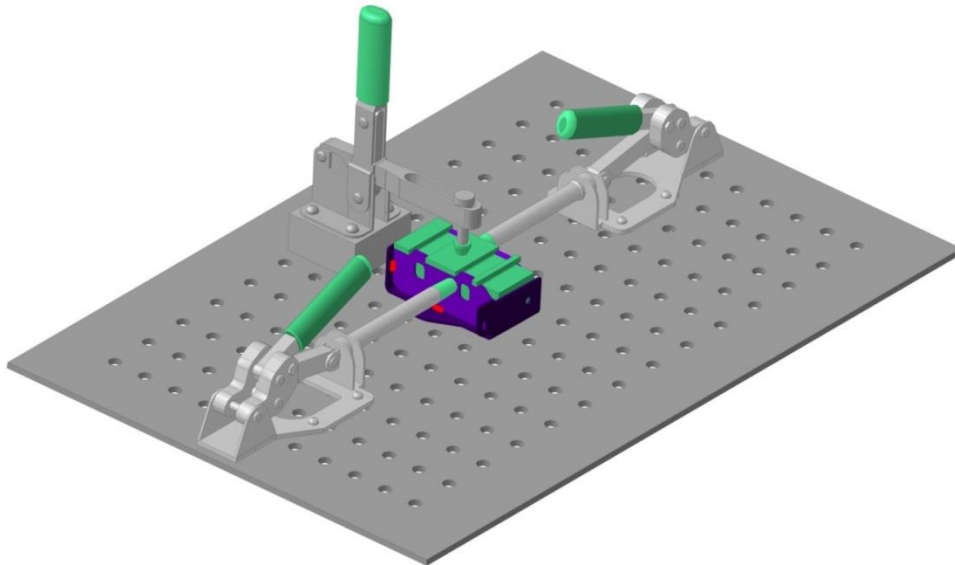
Схема сборки-сварки с универсальными рычажными прижимами
